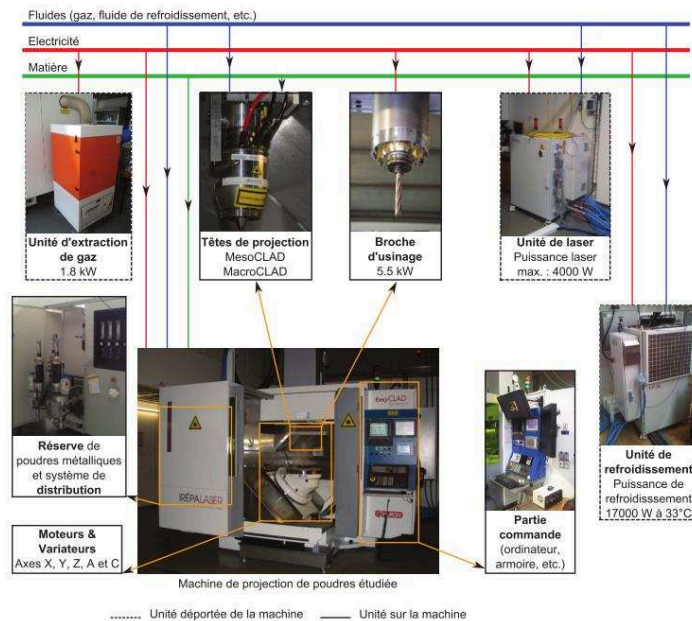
Ensemble des éléments nécessaires à la fabrication par projection de poudres (Le Bourhis, 2014)
